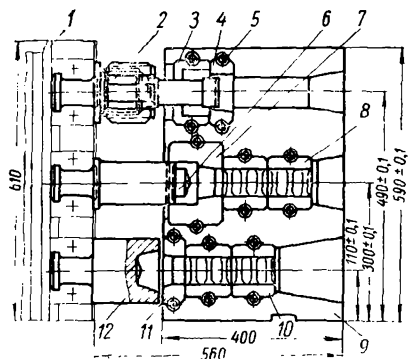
Высадочный штамп для поковки вида кольца: 1 — блок пуансонов; 2 — сборный прошивной пуансон; 3, 4 — прошивные вставки; 5 — винт для вставок; 6 — формовочный пуансон; 7 — формовочная вставка; 8, 10 — зажимные вставки; 9 — матрица; 11 — подъемная вставка; 12 — наборный пуансон
